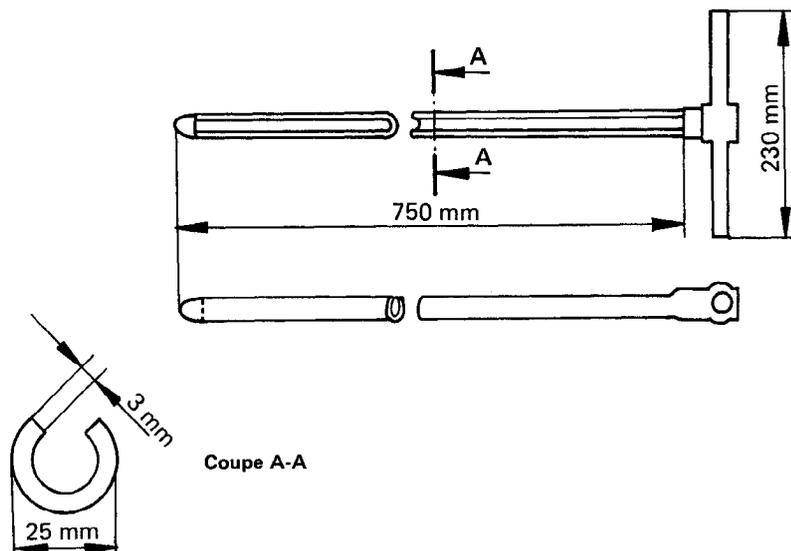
Sonde d'échantillonnage à bout fermé — Dimensions types
